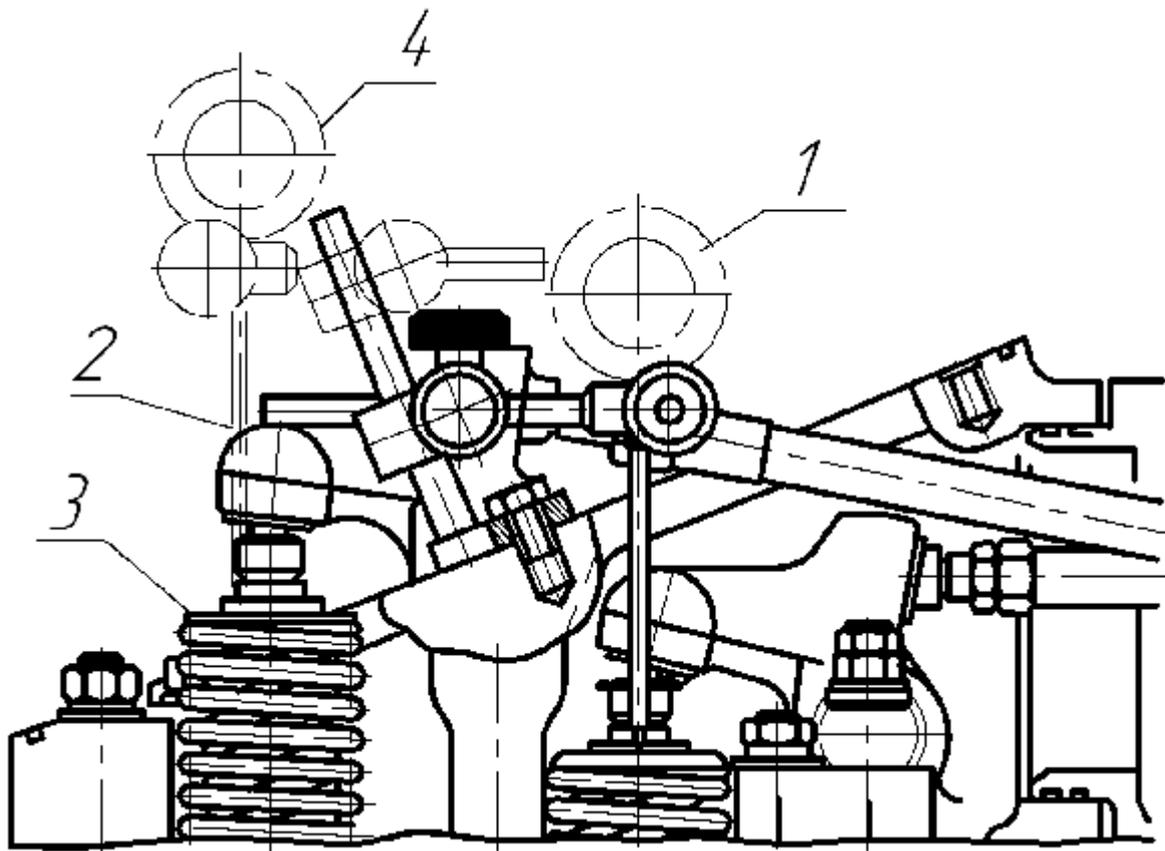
Приспособление для проверки фаз газораспределения: 1 – индикатор часового типа; 2 – шток индикатора; 3 – тарелка клапана
